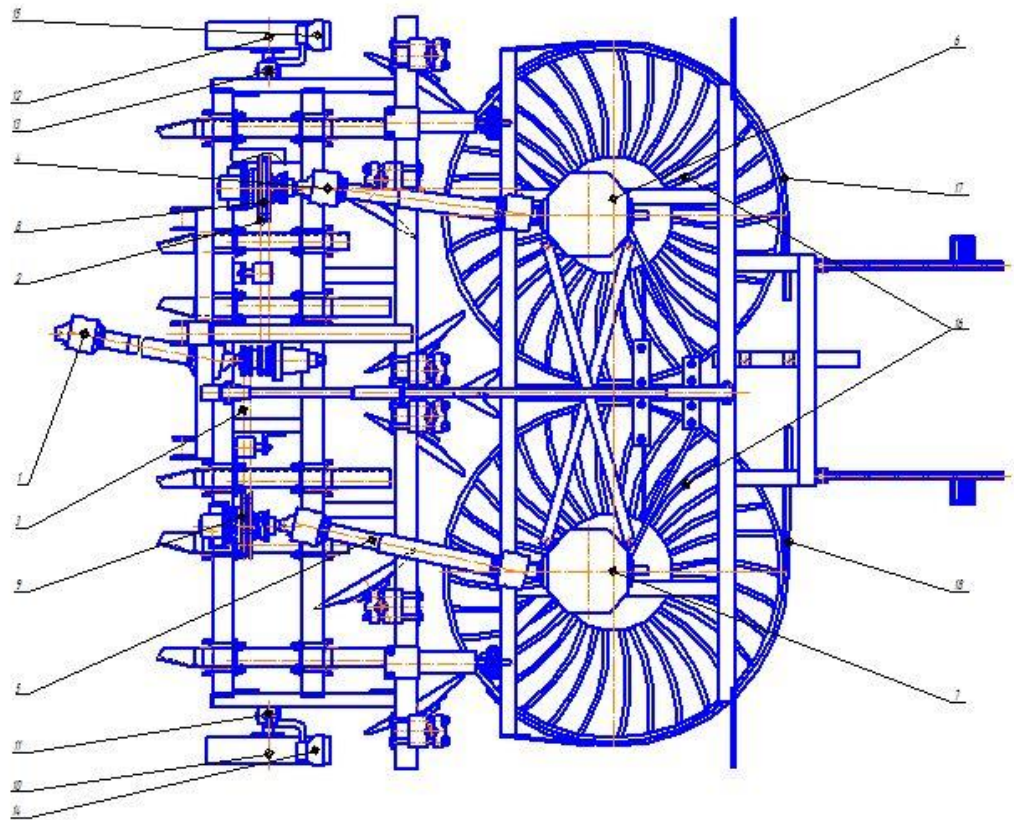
Схема модернізованого копача АЗБ-6 (вид зверху): 1 – вал карданний; 2, 3 – передачі ланцюгові; 4, 5 – карданні контрприводу турбін; 6, 7 – конічні редуктори; 8, 9 – муфти; 10, 12 – опорні колеса; 11, 13 – механізм регулювання положення коліс; 14, 15 – чистики; 16 – турбінні очисники–підбирачі
